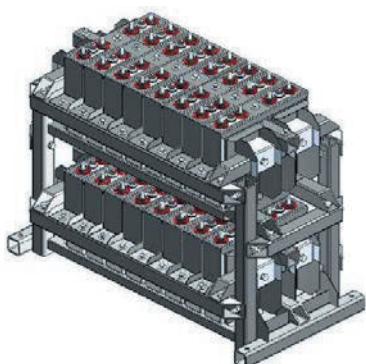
Внешний вид устройства СА-У1
